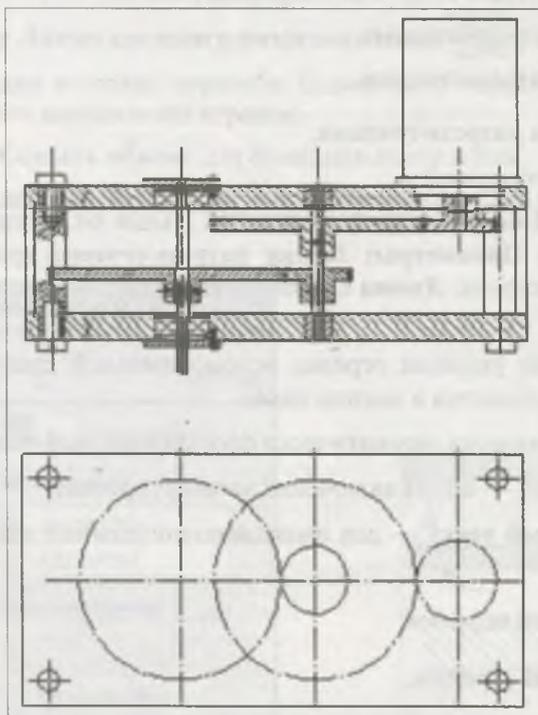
Вариант компоновки сборочного чертежа Редуктор
